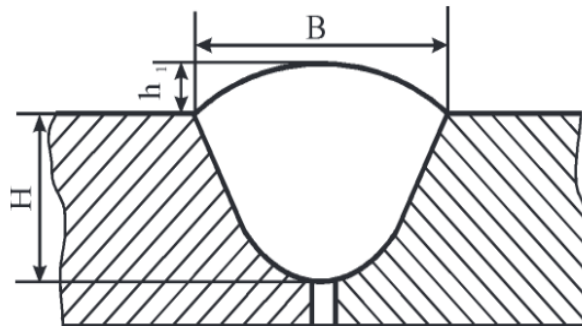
Форма поперечного перерізу зварного шва стикового з'єднання
